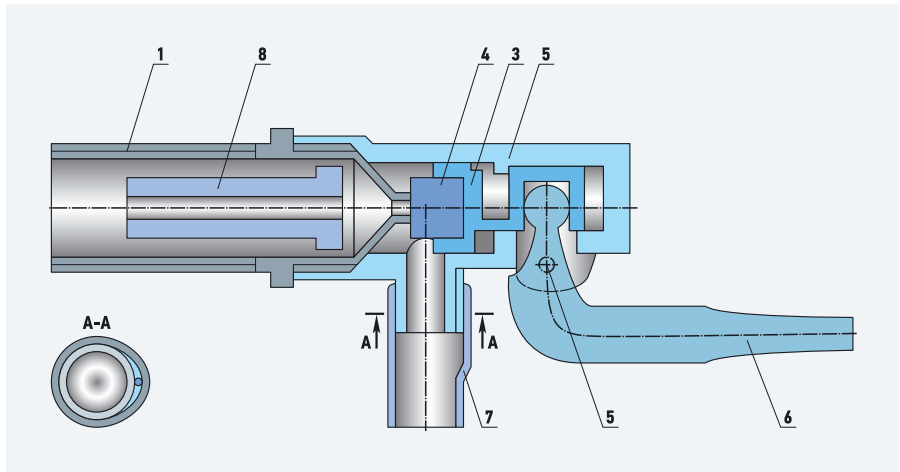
Схема пластмассовой головки наполнительной арматуры [1 — штуцер с соплом; 2 — насадка; 3 — пластмассовый шток; 4 — уплотнительная прокладка; 5 и 6 — ось и рычаг из оцинкованной стали; 7 — противозвонная резиновая трубка; 8 — трубка (ламинарный гидродроссель)]
